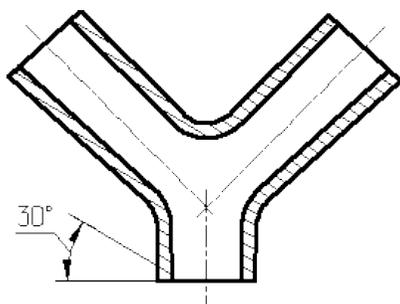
Штриховка под углом 30° к рамке чертежа
